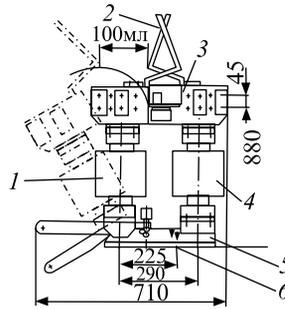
Разъединитель контактной сети постоянного тока РКЖ-3,3/3000: 1 — подвижный изолятор; 2 — дугогасящие рога; 3 — главная токоведущая система; 4 — неподвижный изолятор; 5 — цоколь; 6 — болт заземления
